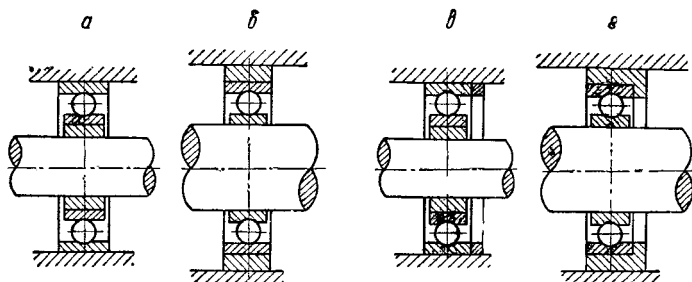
Установка шариковых и роликовых подшипников с ремонтными втулками и кольцами:
